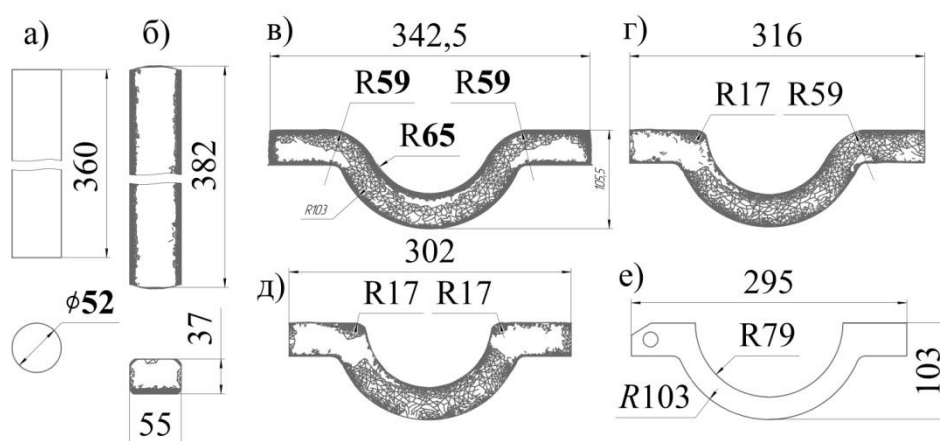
Пооперационное изменение заготовки: а - исходная заготовка; б- заготовка после операции формоизменения; в- после операции гибки; г- калибровка левой полки; д- калибровка правой полки, е- готовая деталь
